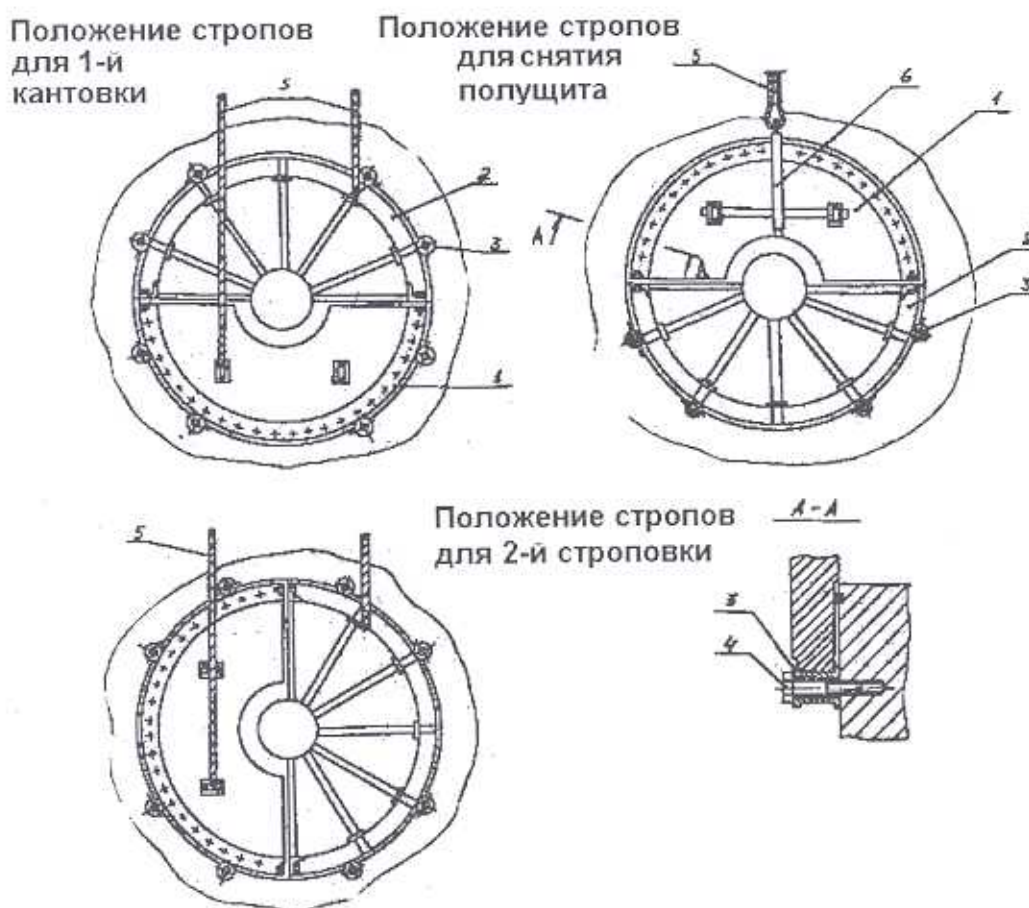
Схема кантовки нижнего полушита статора при разборке:
